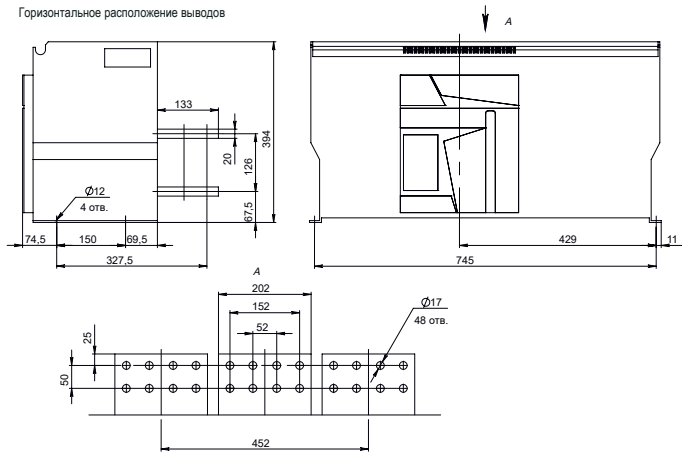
Габаритные размеры выдвигающихся четырехполюсных выключателей типоразмера Н
